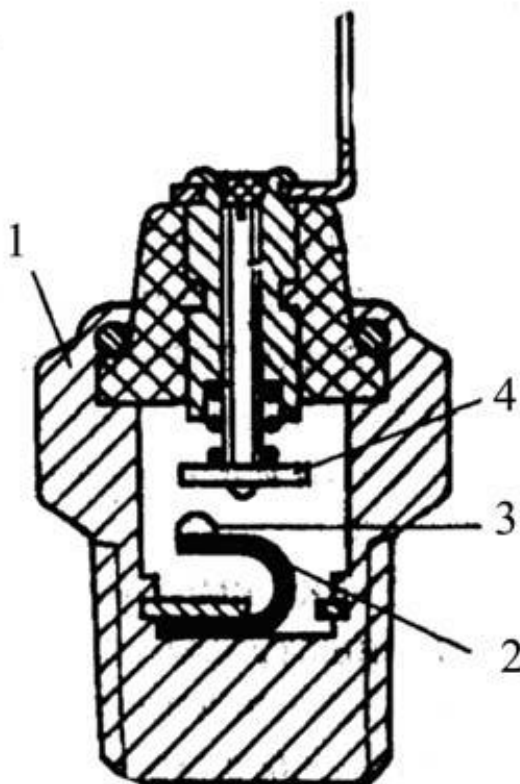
Конструкция датчика ТМ108: 1-корпус; 2-термобиметаллическая пластина; 3-подвижный контакт; 4-неподвижный контакт.
